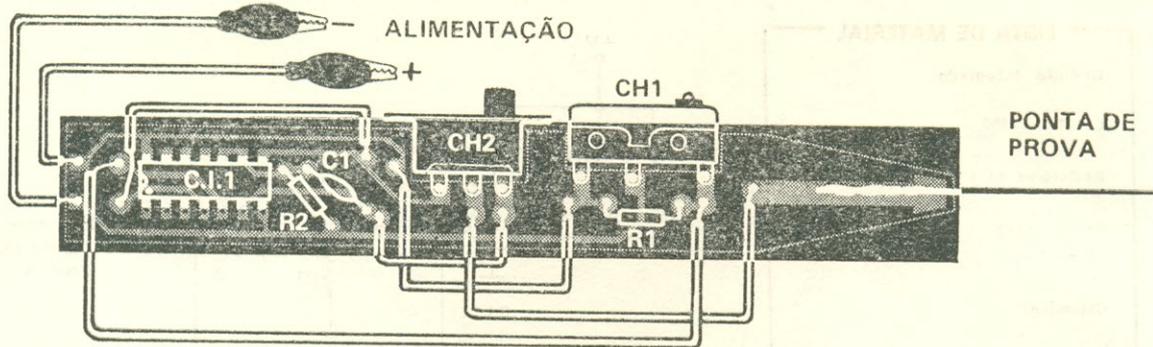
Disposição dos componentes sobre a plaqueta da Fig. 4.
